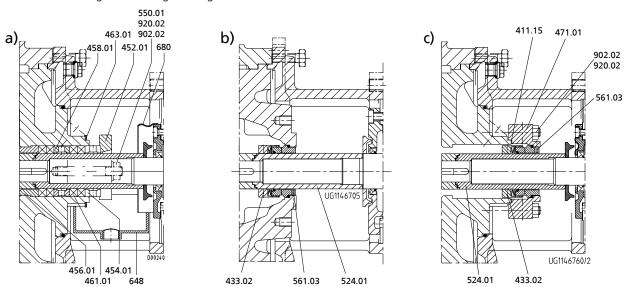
(a Ausführung mit Stopfbuchspackung , b) Gleitringdichtung mit konischem Gehäusedeckel, c) Gleitringdichtung mit zylindrischem Gehäusedeckel
